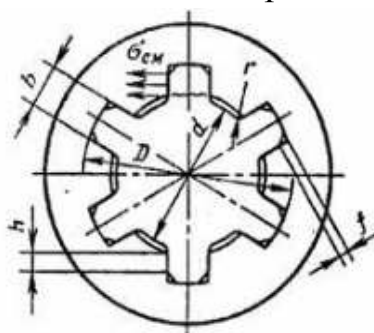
Схема поперечного сечения шлицевого соединения
